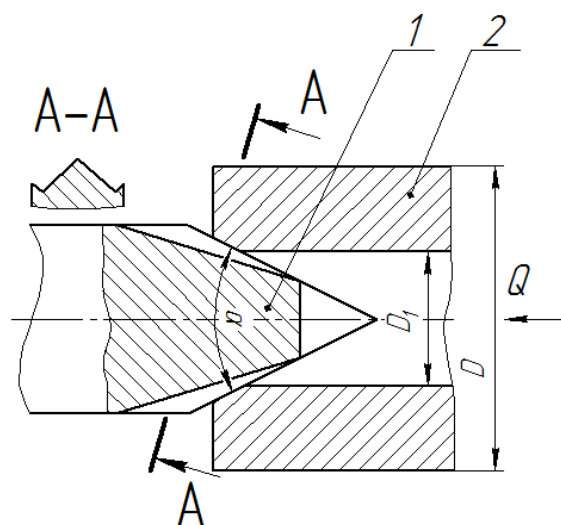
Будова зубчастого повідкового центра: 1 – зубчастий центр; 2 – деталь
